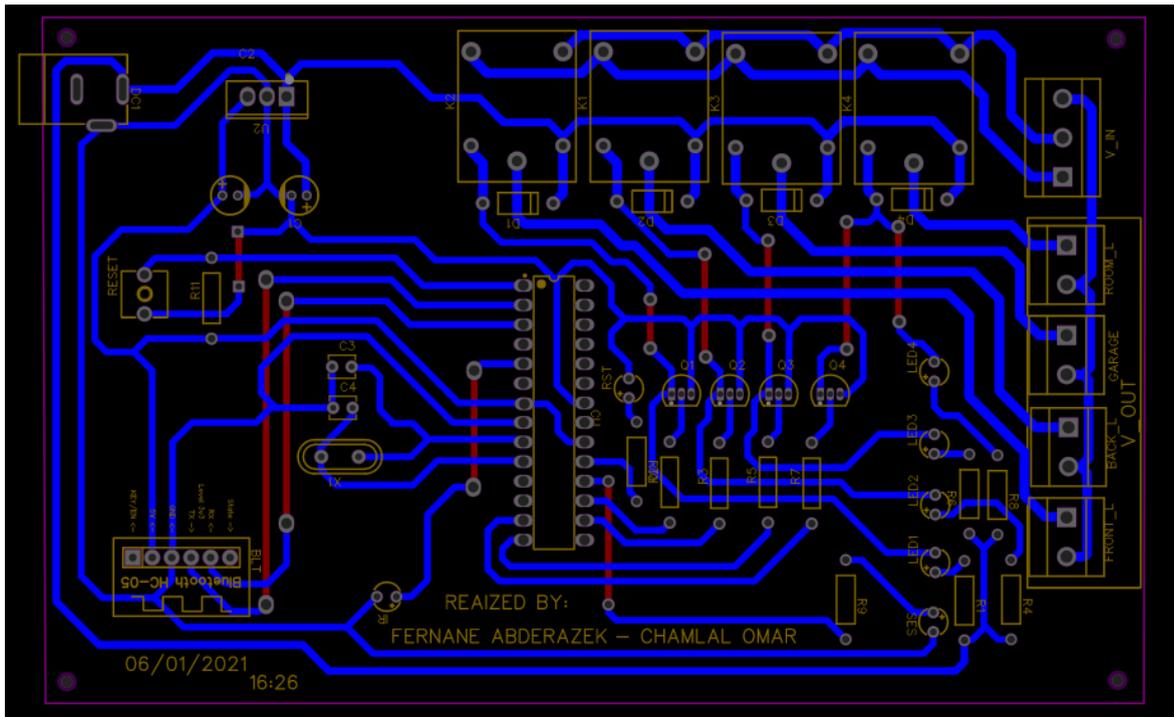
Carte PCB avec un Arrière-plan Noir
